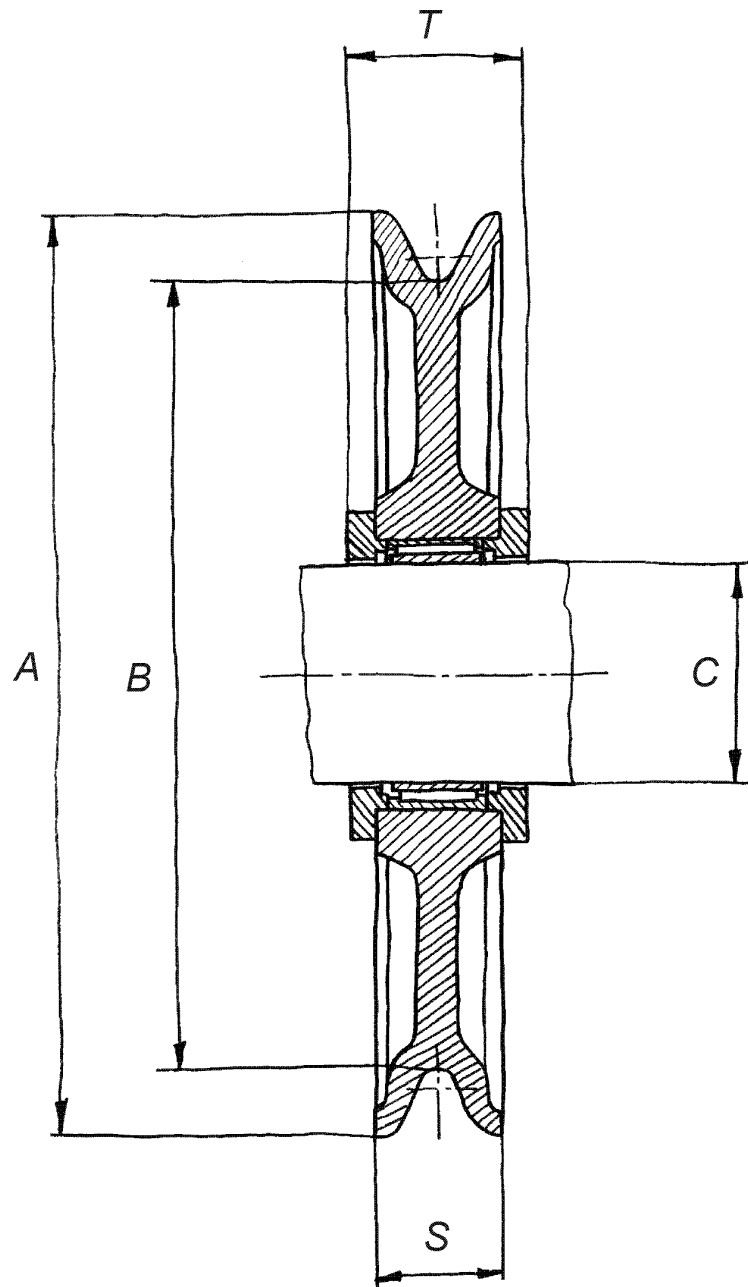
Dimensioni principali carrucola con cuscinetto a rullini e boccole flangiate in bronzo.
